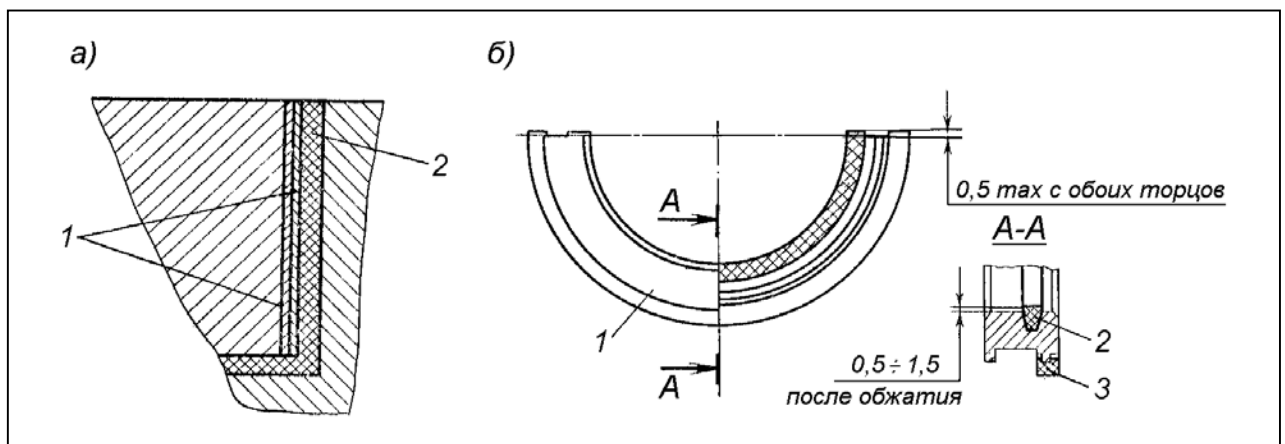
К сборке пятого коренного подшипника двигателей Д-65 и модиф:
